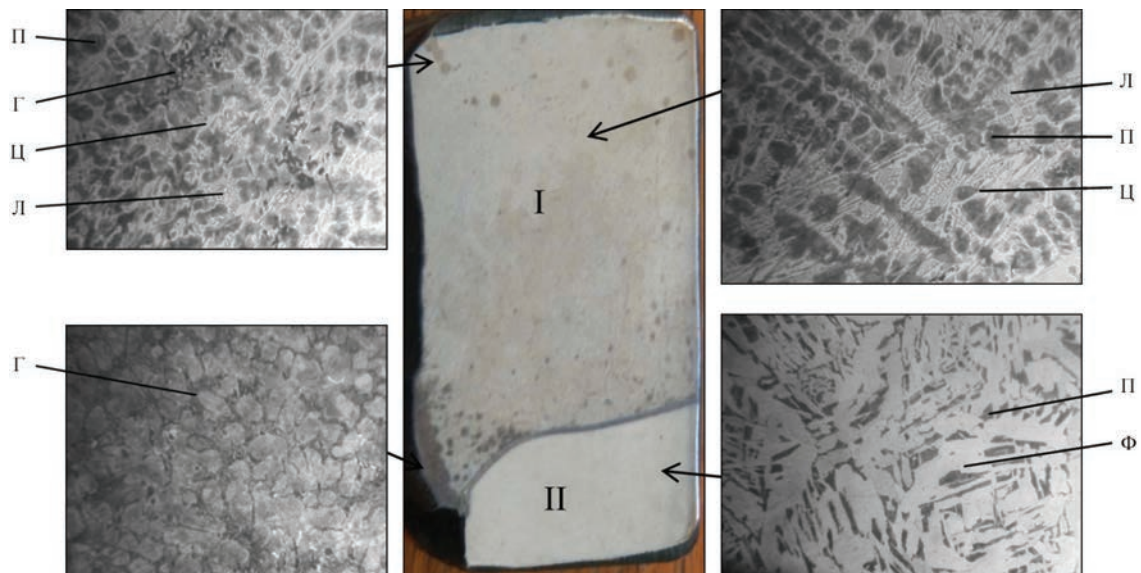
Микроструктура ($\times 100$) наплавленного металла микрошлифа № 1: I — наплавленный металл; II — основной металл
